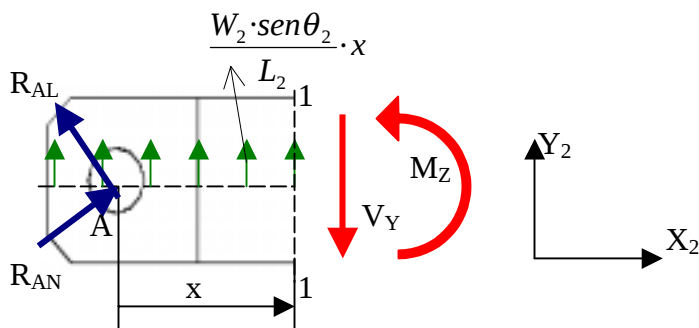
Corte 1-1 en el eslabón 2. Plano XY
